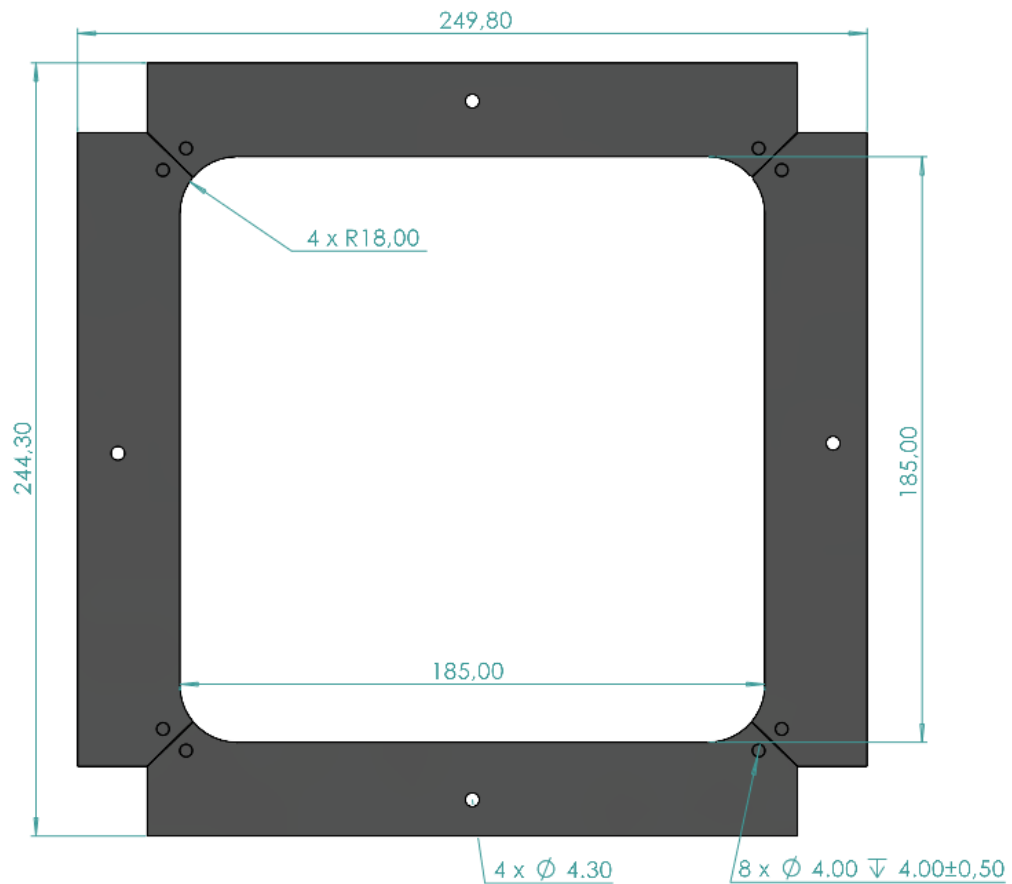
Dimensões geométricas – Vista de topo do adaptador
